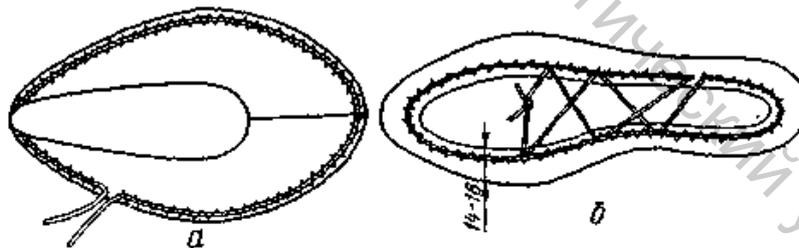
Схемы пристрачивания льняной нитки к заготовке верха (а) и шнуровочная затяжка (б)
